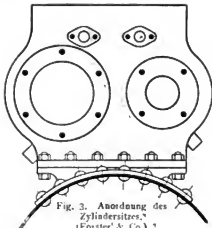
Anordnung des Zylindersitzes. (Forster & Co.)
